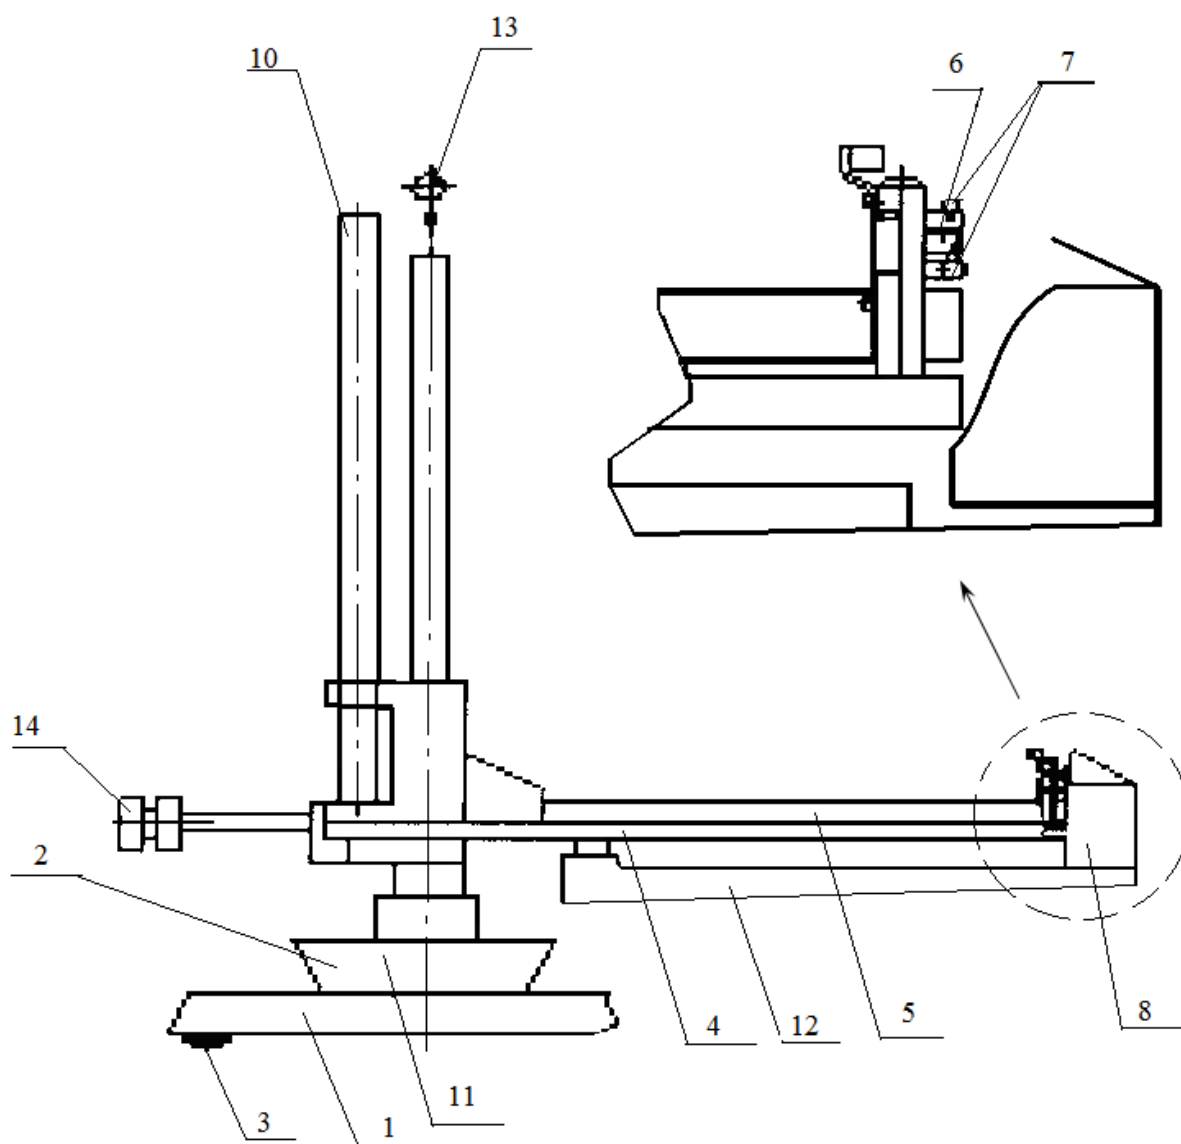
Сборочный чертеж установки ТМд-06м
